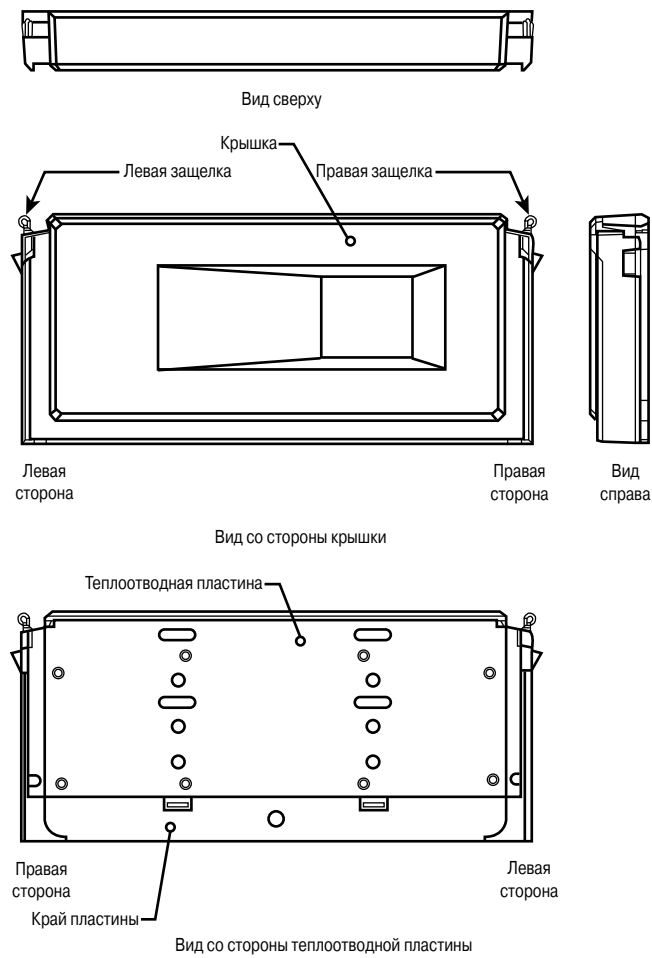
Детали корпуса SEC для процессора Pentium II
